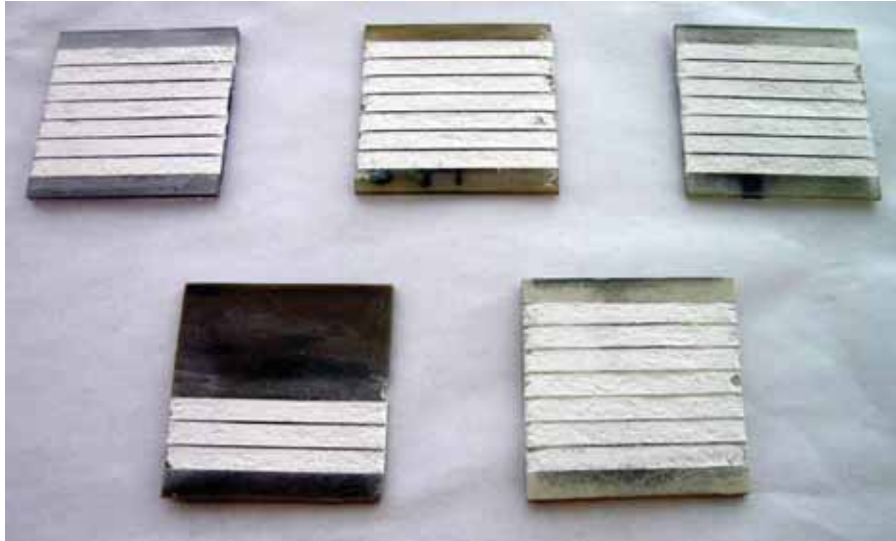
Gefräste Versuchsplatten mit Füllmaterial in den Fräsbahnen
